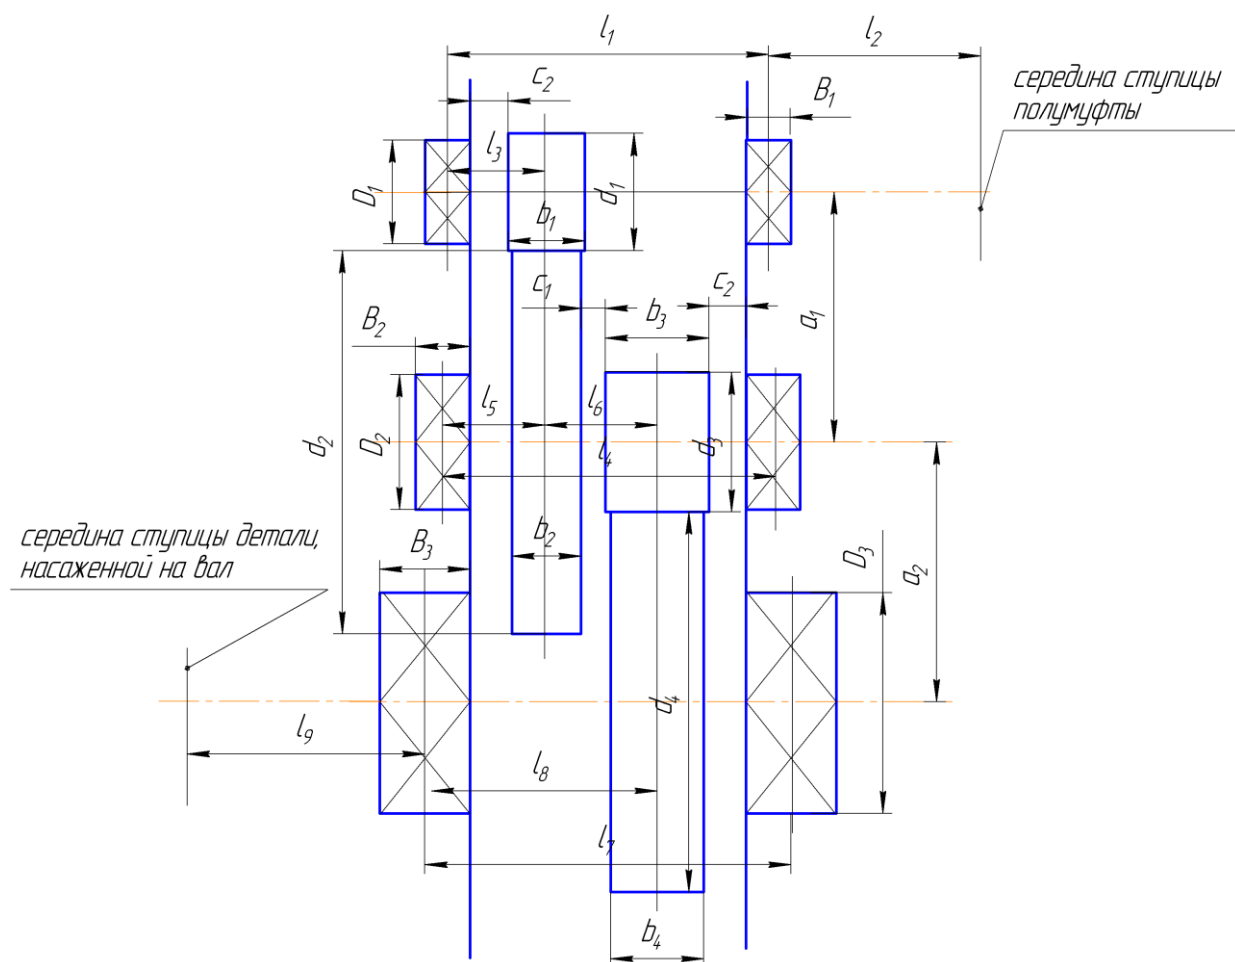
Компоновка двухступенчатого цилиндрического редуктора (смазка подшипников – масляным туманом)
